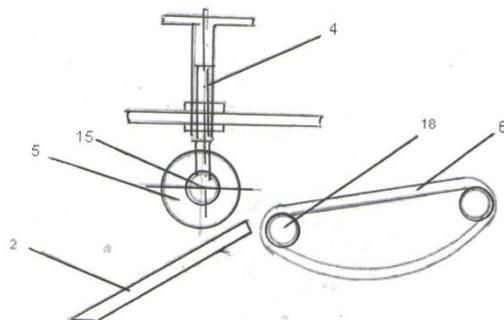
Положение рыхлителя с регулировочным винтом относительно лемеха: 2 – лемех; 5 – рыхлитель; 15 – вал; 4 – винт регулировочный; 18 – вал скоростного пруткового элеватора; 6 – скоростной прутковый элеватор
